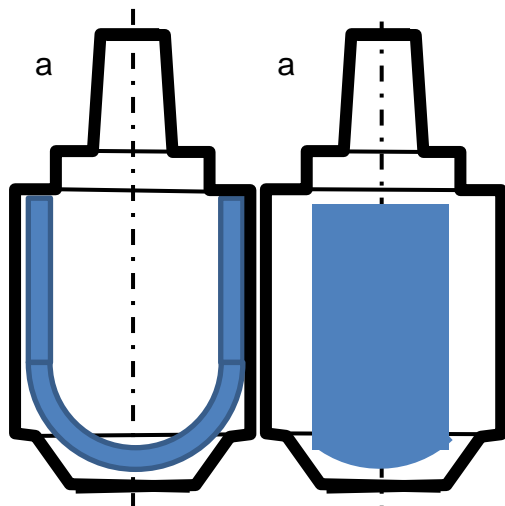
Prinzipielle Lage des zweipoligen Tulpenmagneten im Gehäuse
